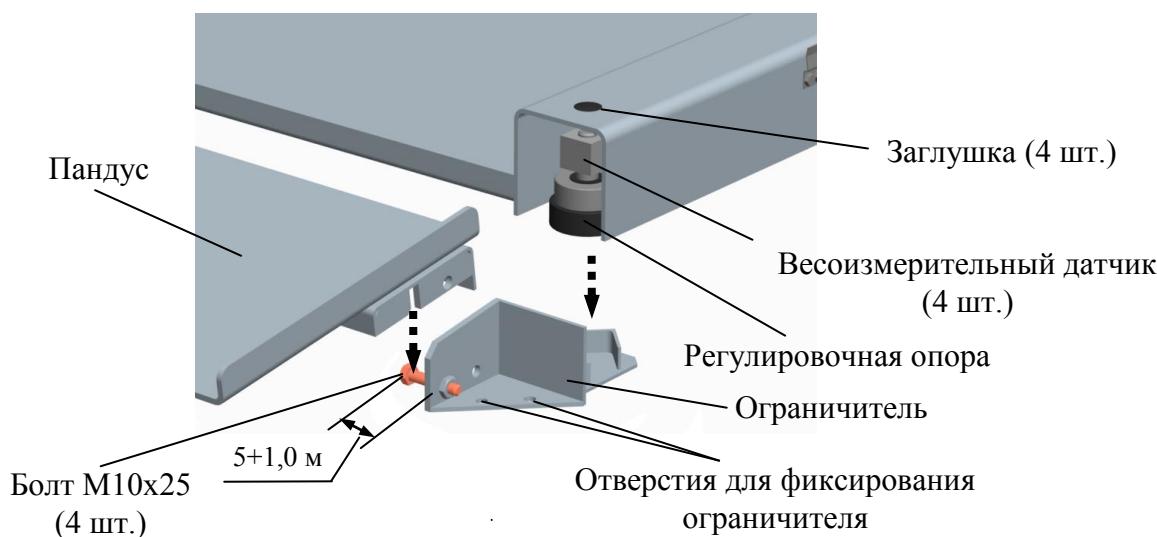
Сборка модуля взвешивающий 4D-LA
